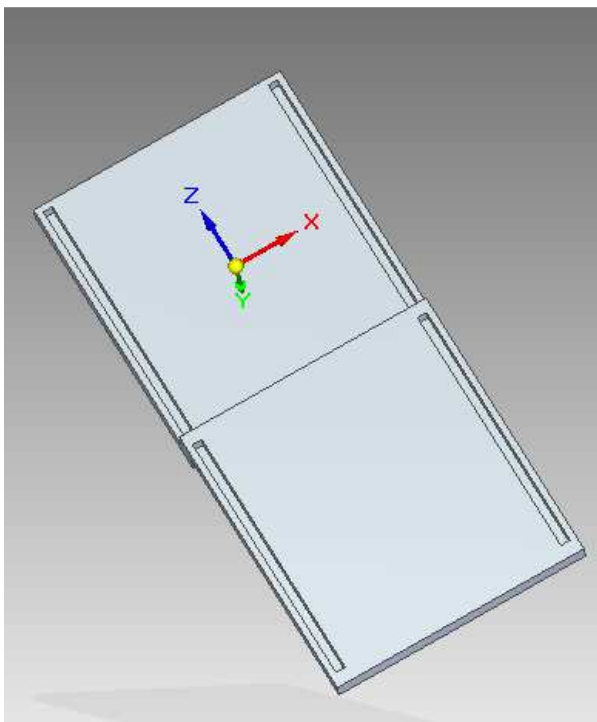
SEGUNDA PARTE DE LA PUERTA TELESCÓPICA UNIDA A LA PRIMERA
